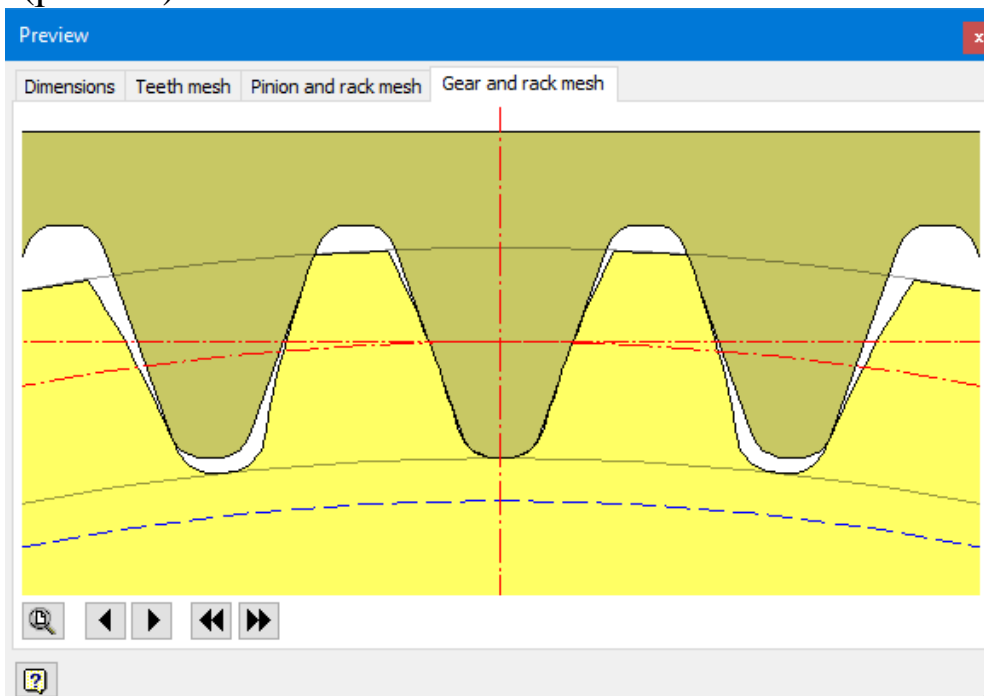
Двовимірний кресленник зачеплення зубчастого колеса і верстатної рейки
